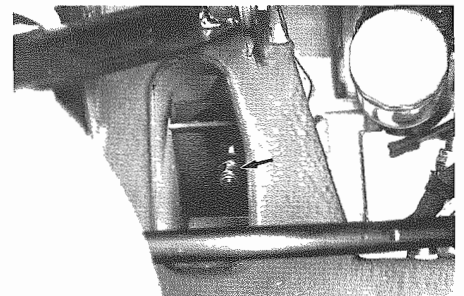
Viti di fissaggio laterale motore - Side engine screws
